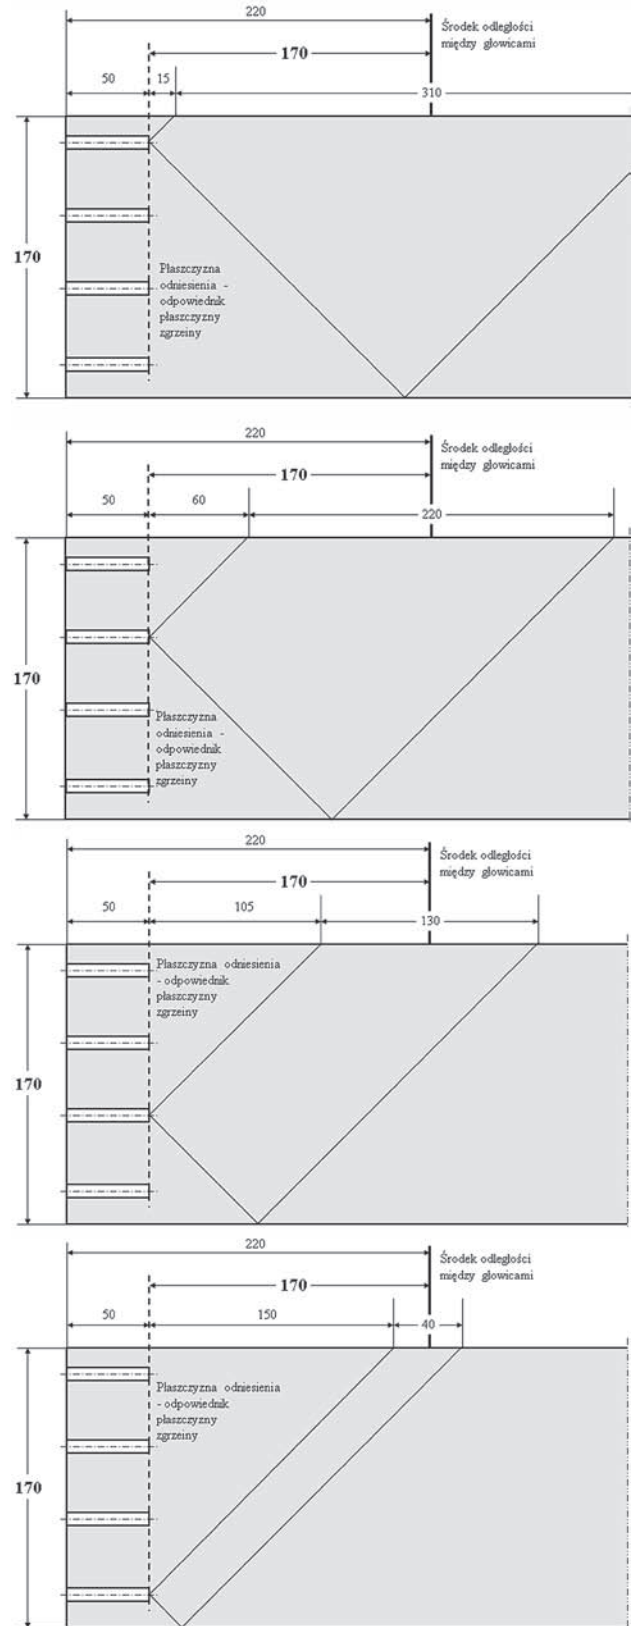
Przykład wykorzystania ultradźwiękowej techniki echa [3].
